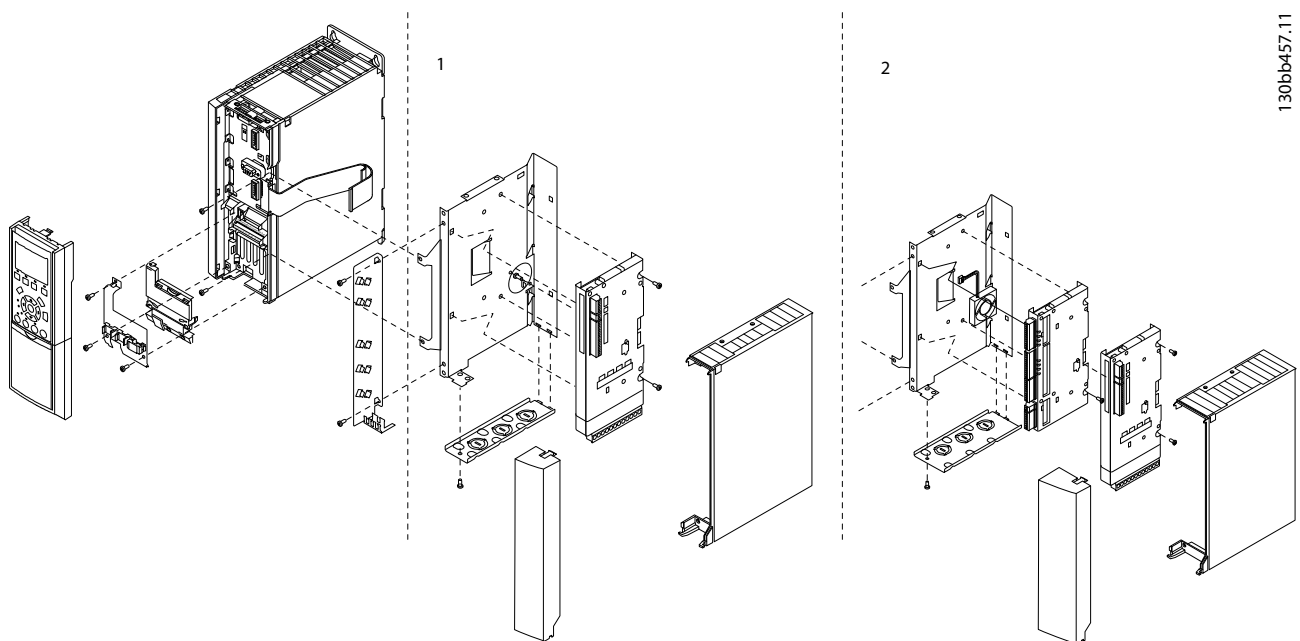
Installation du VLT® Extended Relay Card MCB 113 – Vue éclatée
